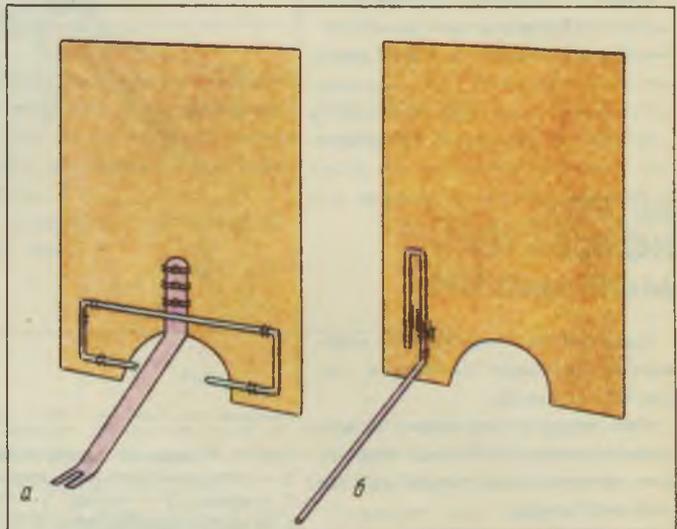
Сборка ветроколебателя: а — крепление каркаса и рычага-колебателя; б — крепление пружины с обратной стороны паруса.
